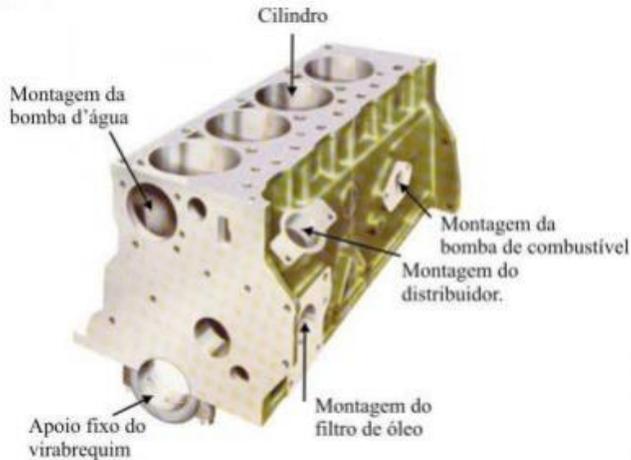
Partes de um motor a diesel, bloco dos cilindros.
